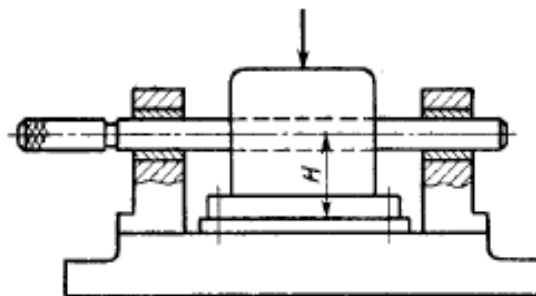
Схема перевірки розточувального пристосування по еталонній деталі
